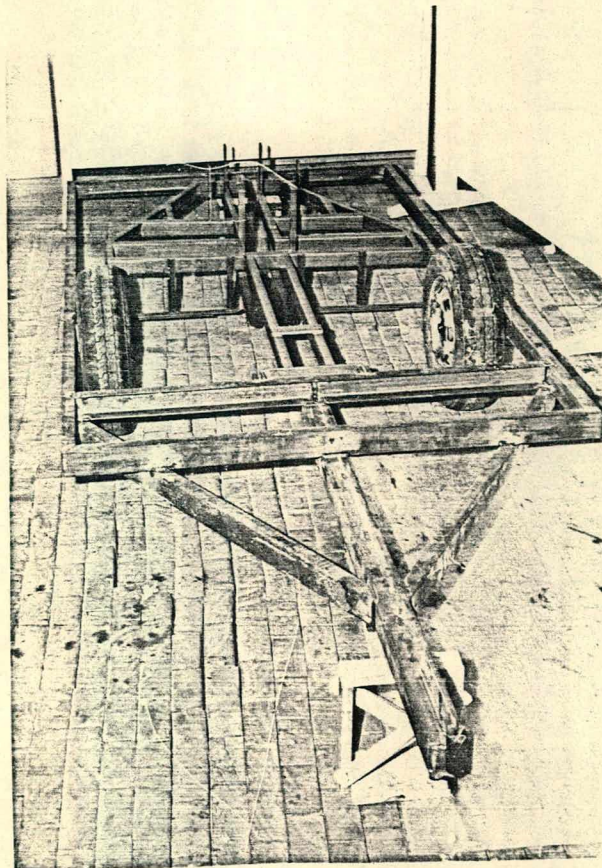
Detalhe da montagem do chassi da carreta.
